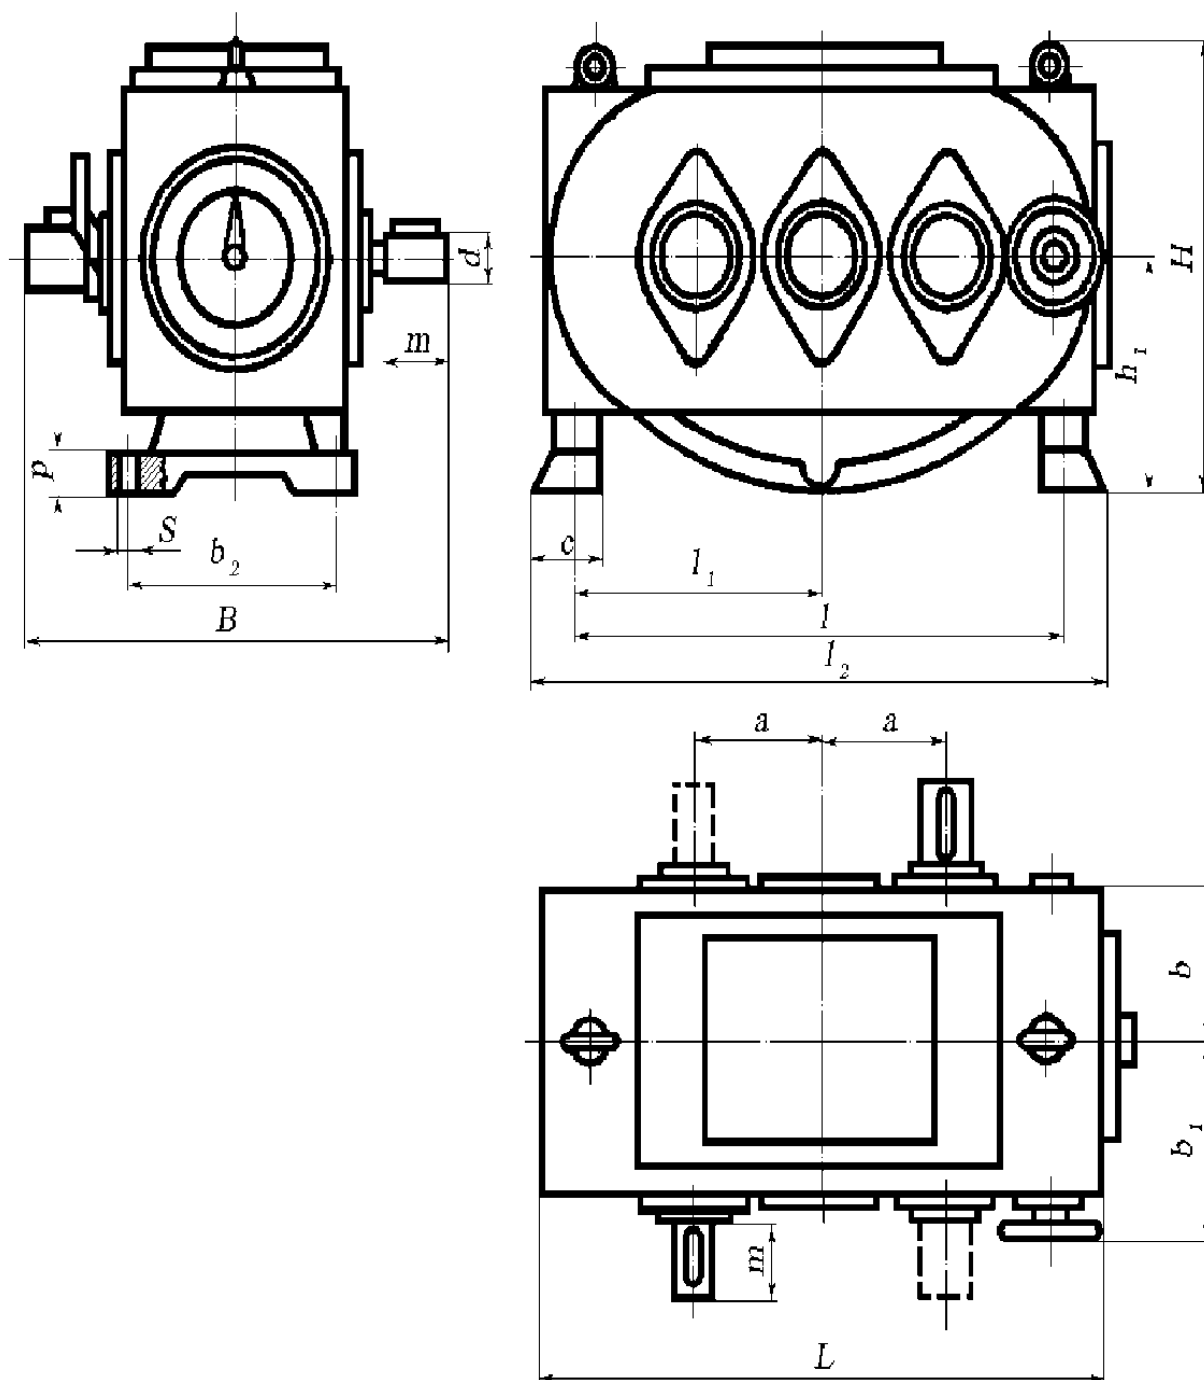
Габаритные и присоединительные размеры цепных пластинчатых вариаторов
